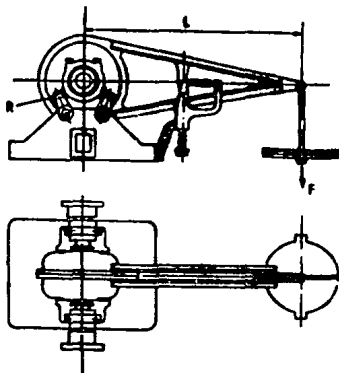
Planta y alzado de un freno dinámómetro hidráulico.
